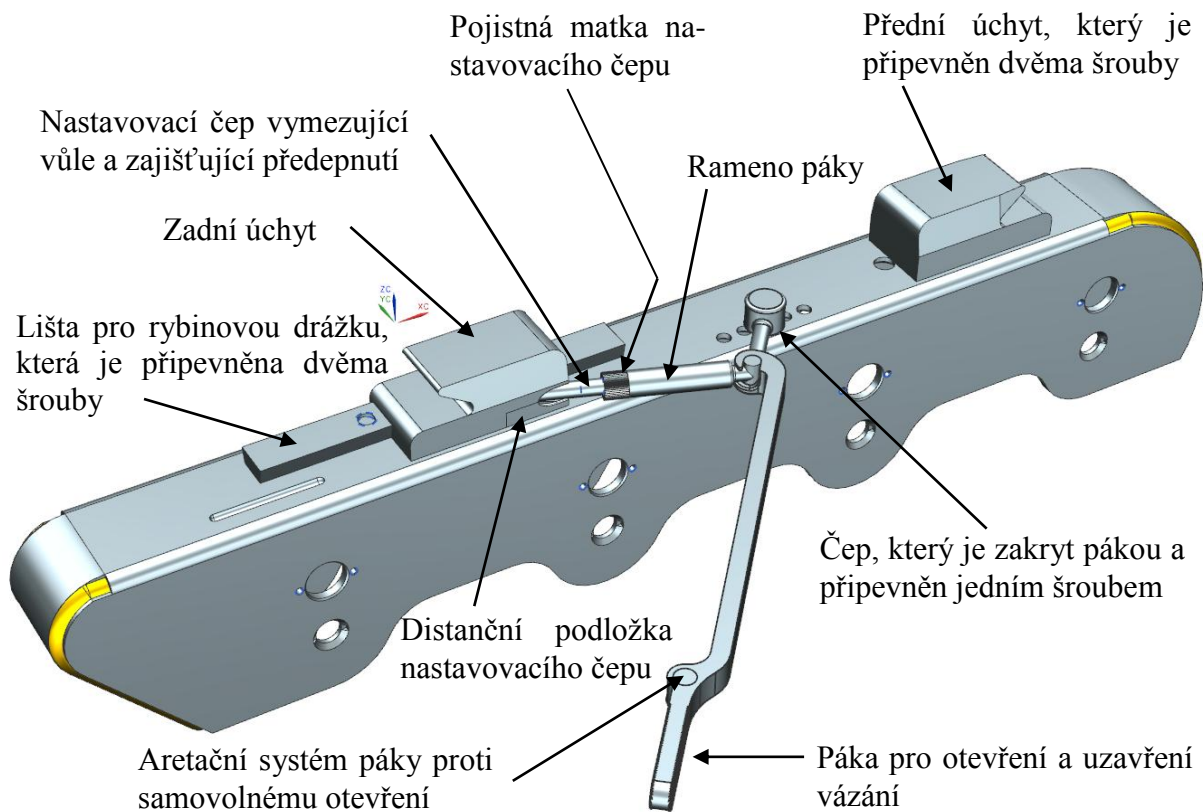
Vložka podrážky zajišťující spojení boty a rámu in-line brusle
